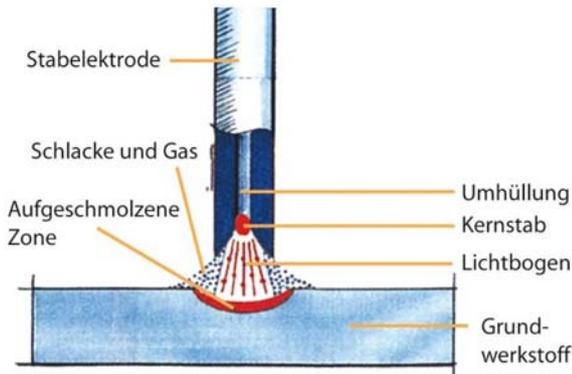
Funktionsprinzip Lichtbogenhandschweißen
